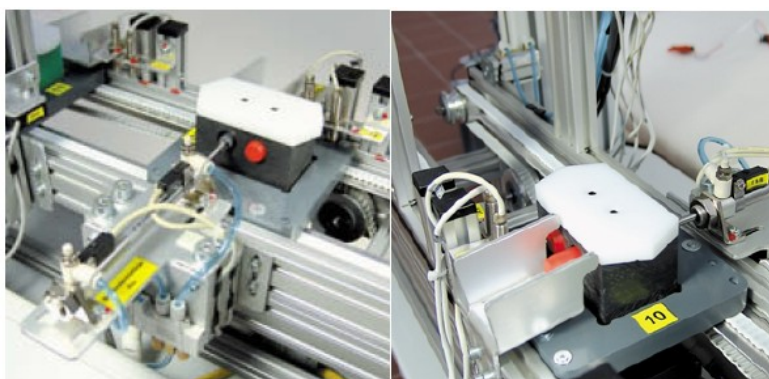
Stația de scoatere a bolțurilor în cadrul operației de dezasamblare
